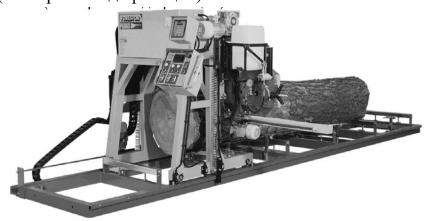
Общий вид бревнопильного ленточнопильного станка
